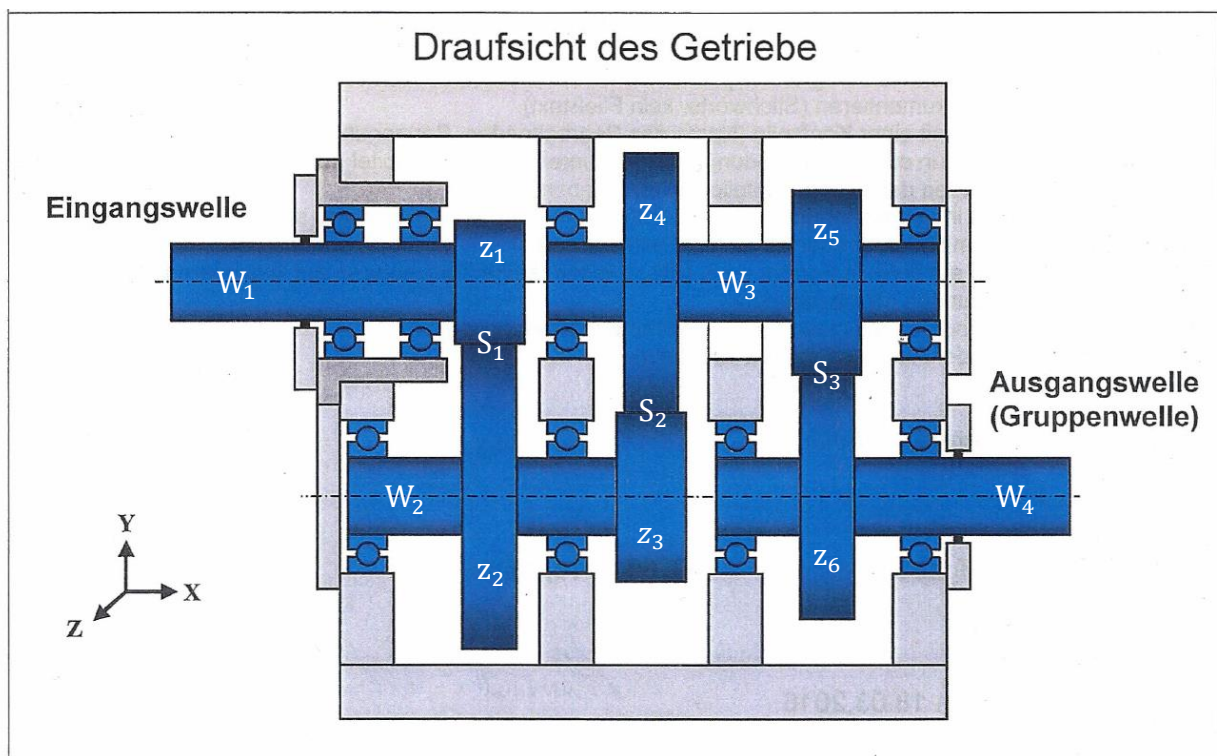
Draufsicht des Getriebes mit Bauteilbezeichnung
